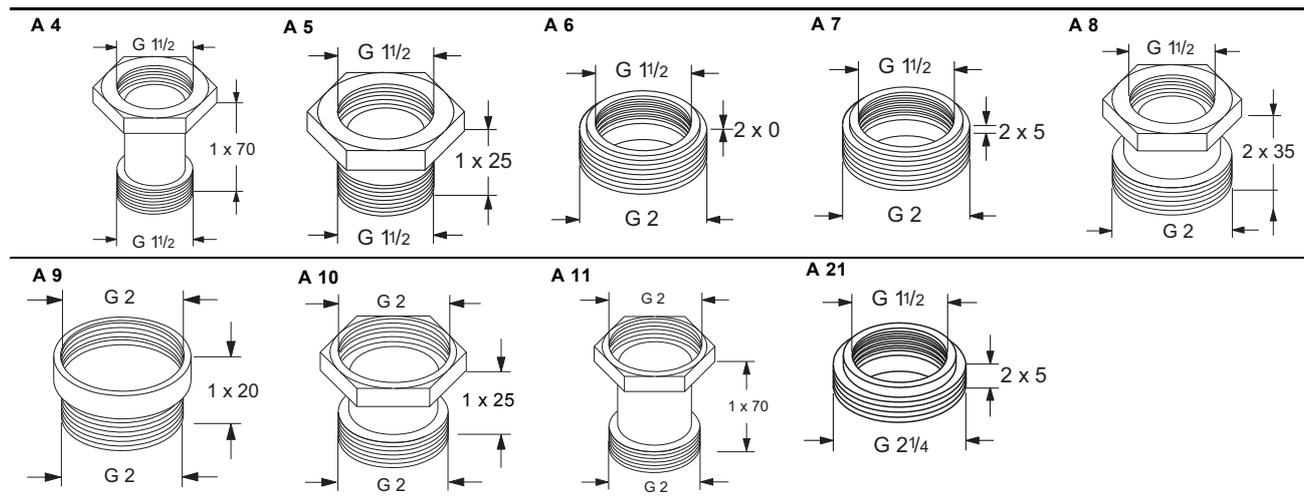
Beispiel eines Gewinde/Gewinde-Adapters
